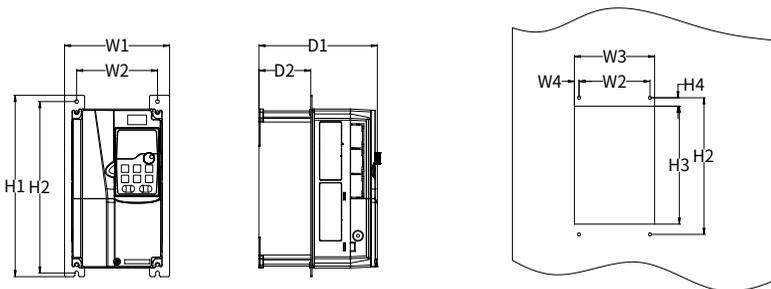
380V 90~110kW 变频器法兰安装及开孔尺寸
